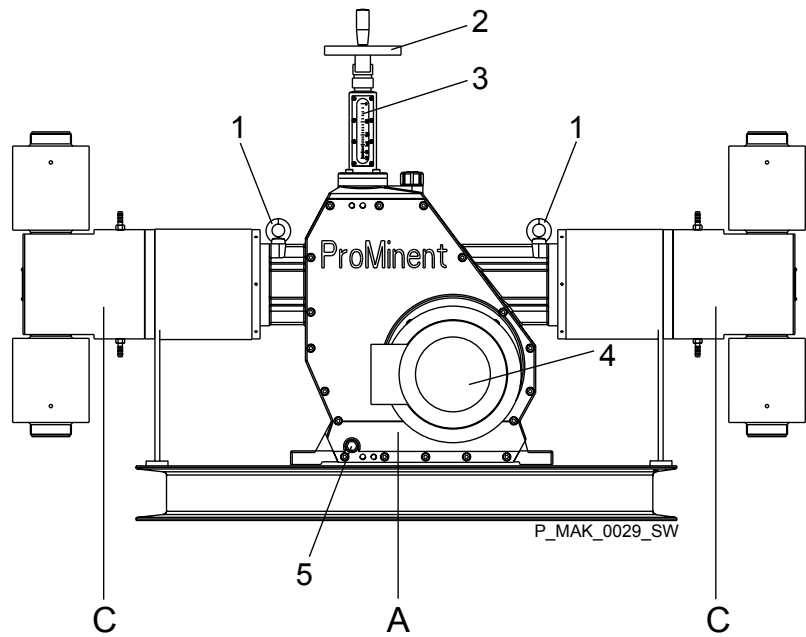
Vista del lado del motor (aquí M5Ka D)
